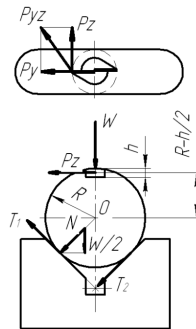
Схема сил при фрезеруванні шпонкового паза
